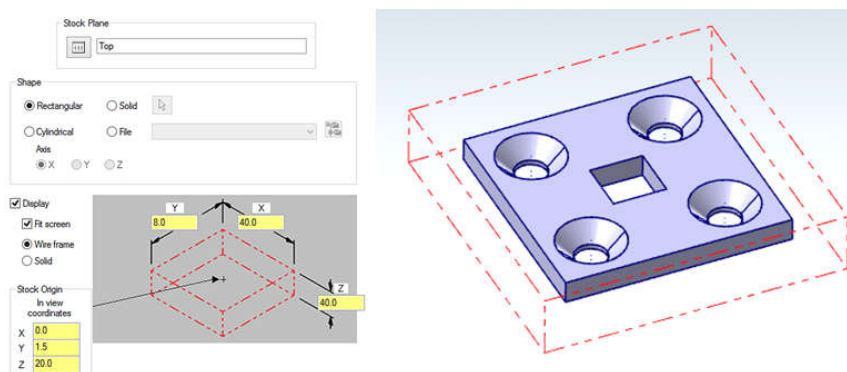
Stock inicial da maquinação da chapa de fixação da agulha modeladora final
